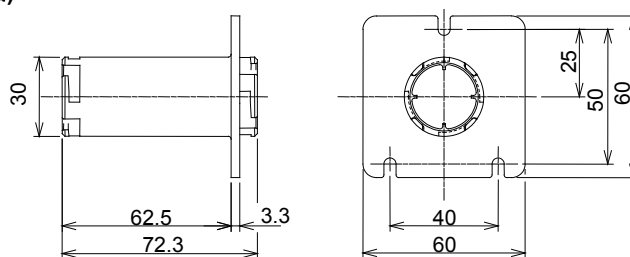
外形尺寸图: Part No. 83157235-001 (mm)
